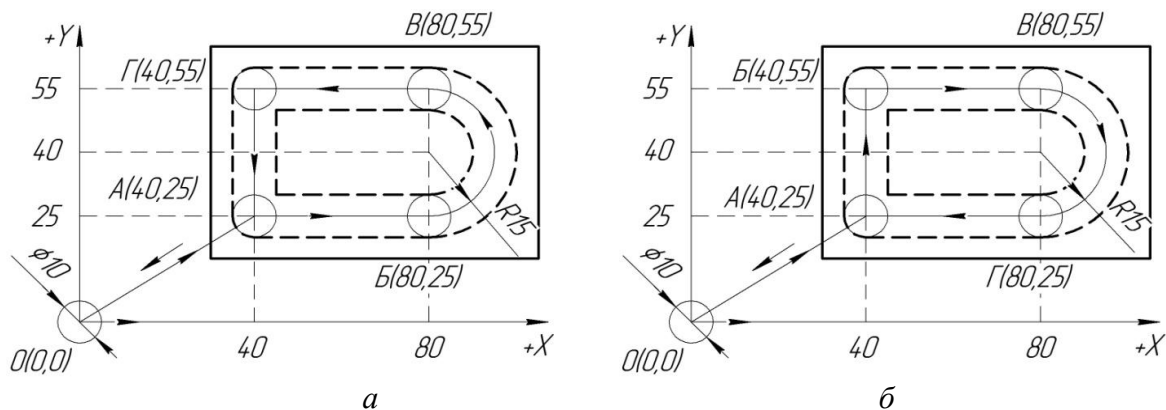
Фрезерування канавки по прямій і півкола проти годинникової (а) і за годинниковою стрілкою (б)
